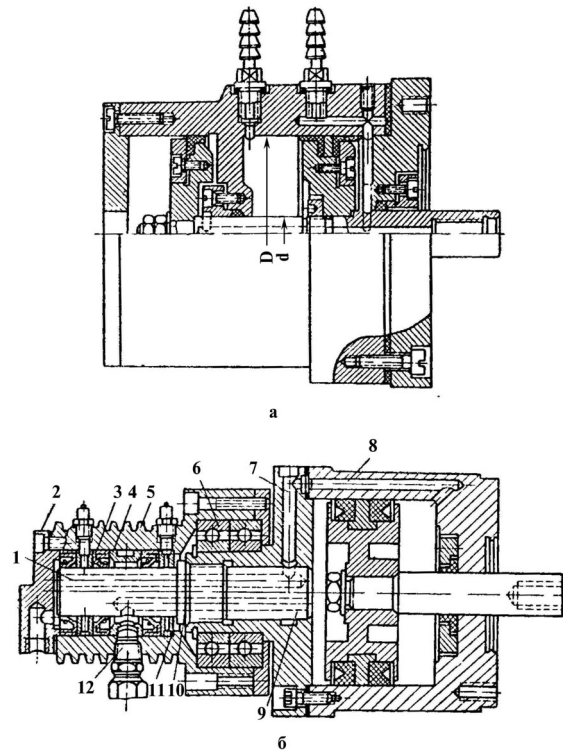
Приклади конструкцій пневмоциліндрів: а - зі здвоєним поршнем; б - обертовий пневматичний циліндр.
